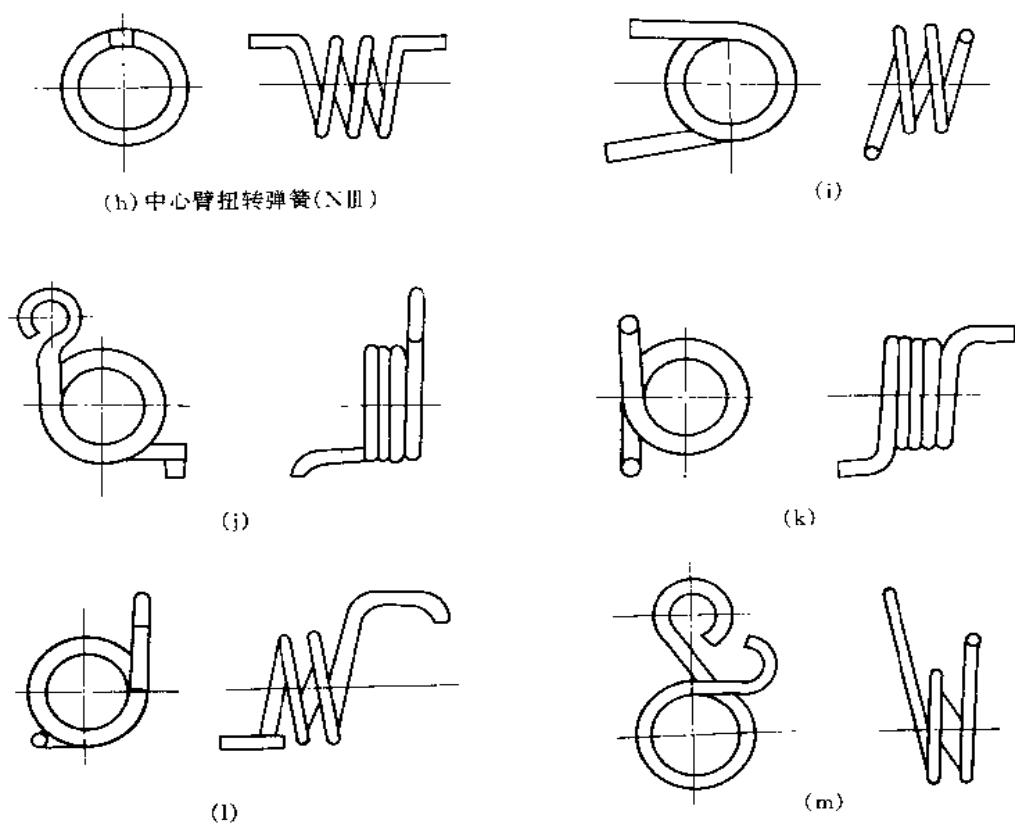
圆柱螺旋扭转弹簧端部结构
